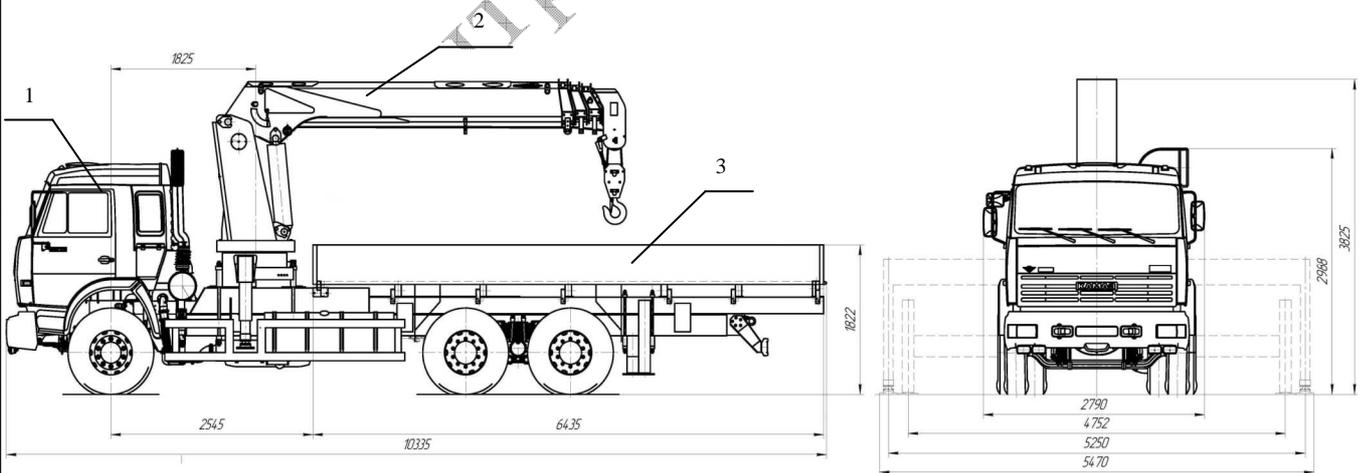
б - Общий вид 333004 на шасси КАМАЗ-65115-62
